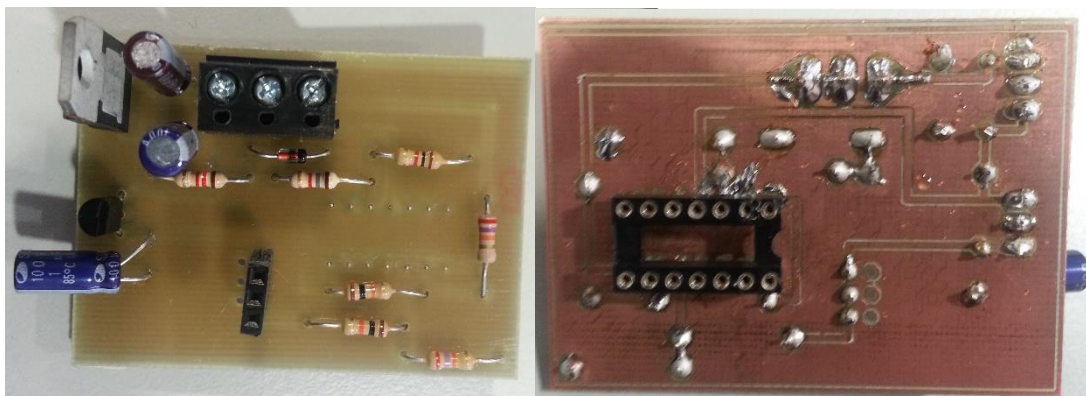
Placa PCB de amplificação do sensor de pressão
